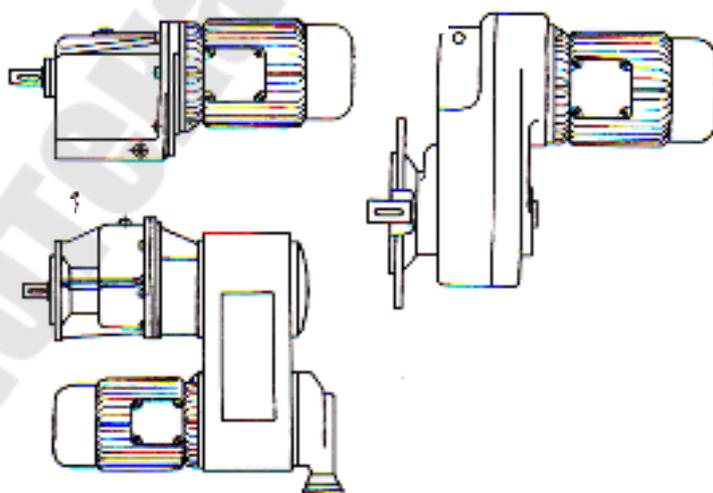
Мотор-редукторы с трехфазными асинхронными электродвигателями
